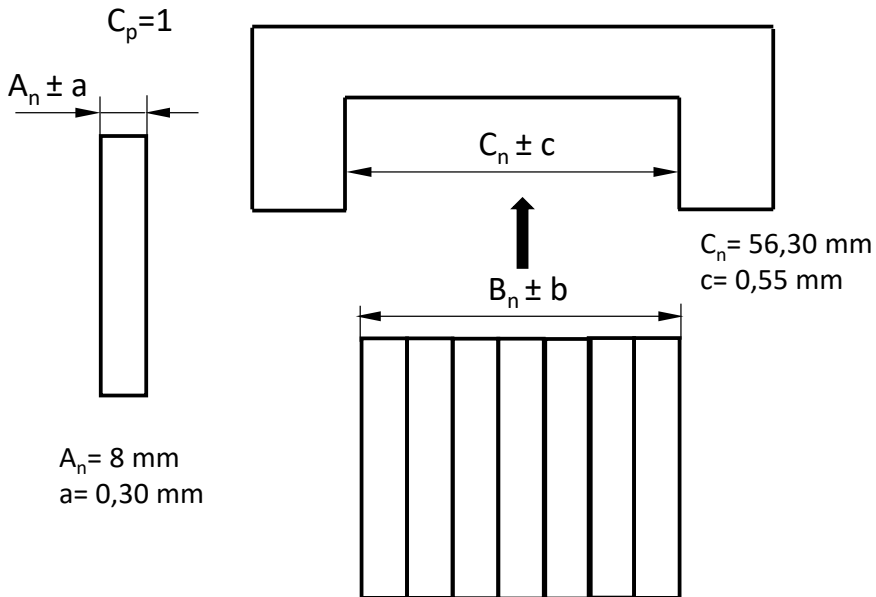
Apilado o “stack” de tolerancias y ensamblaje en elemento contenedor o “bracket”.
